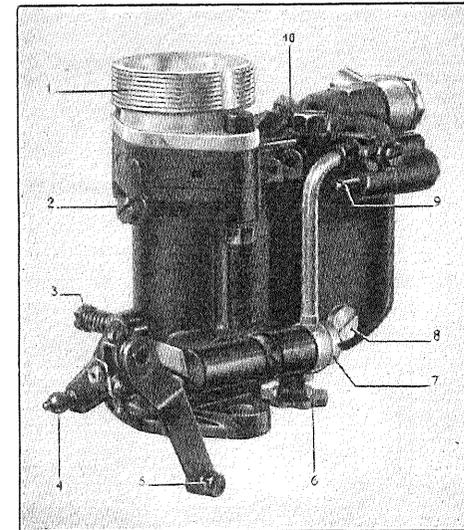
Vista esterna del carburatore Zenith 30 VEIZ.
